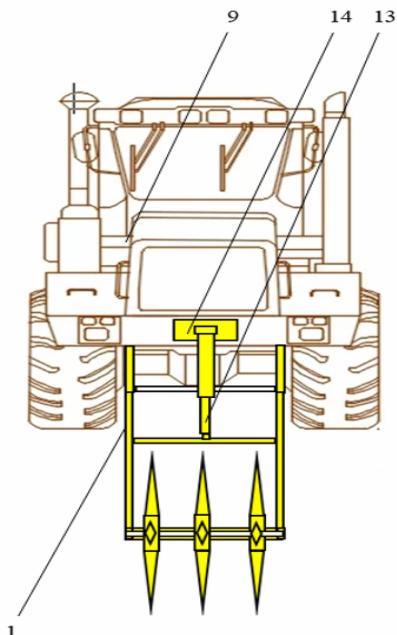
Фронтальный вид колёсного полурамного трактора с установленным фронтальным прокальвателем-щелерезом
